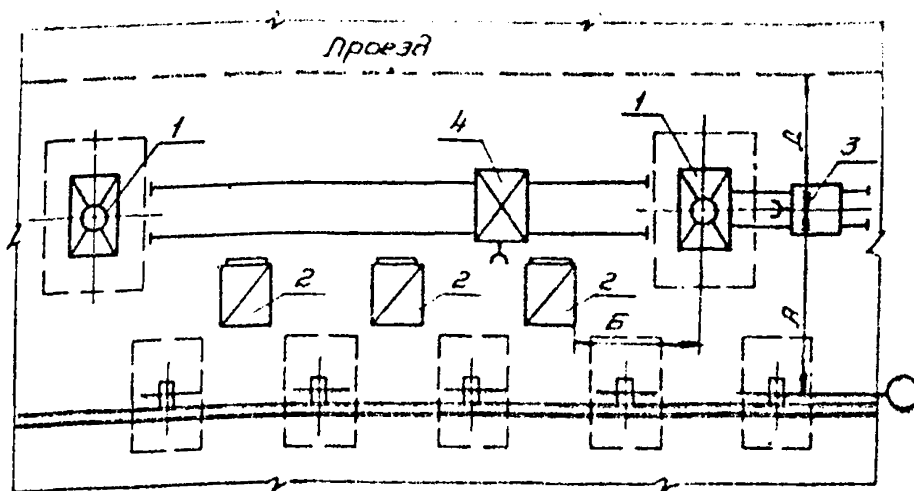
Схема расположения участка паровоздушного ковочного молота с МТЧ 5000 кг:
